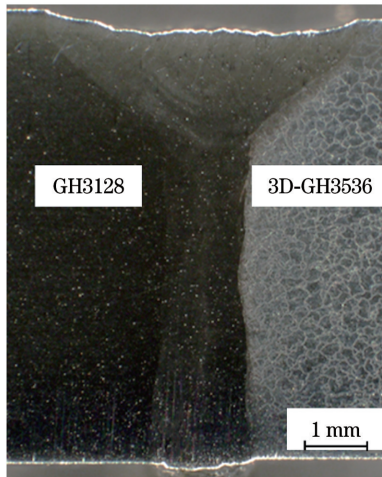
3D-GH3536/R-GH3128 焊缝宏观形貌
